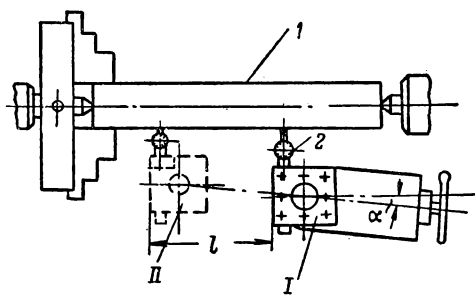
Схема проверки правильности поворота верхних салазок суппорта при помощи индикатора.
